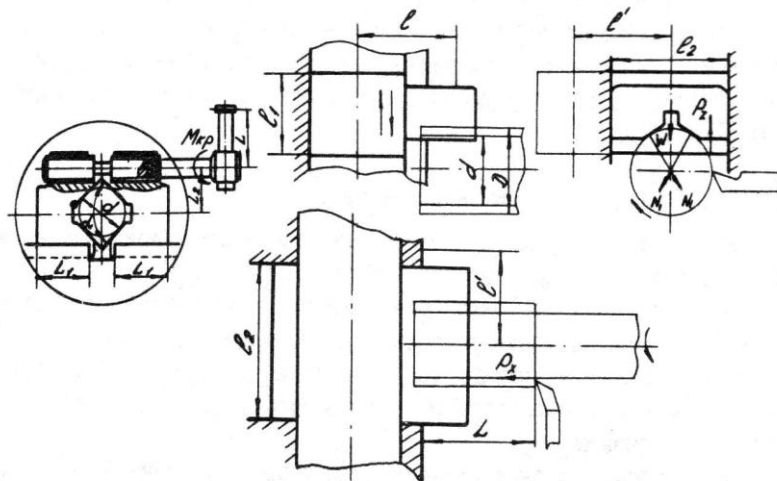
Схема установки заготовки в двохкулачковому патроні
